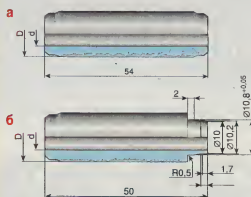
Втулки клапана двигателя 331.10. а – штатная; б – с маслоотражательным колпачком.
